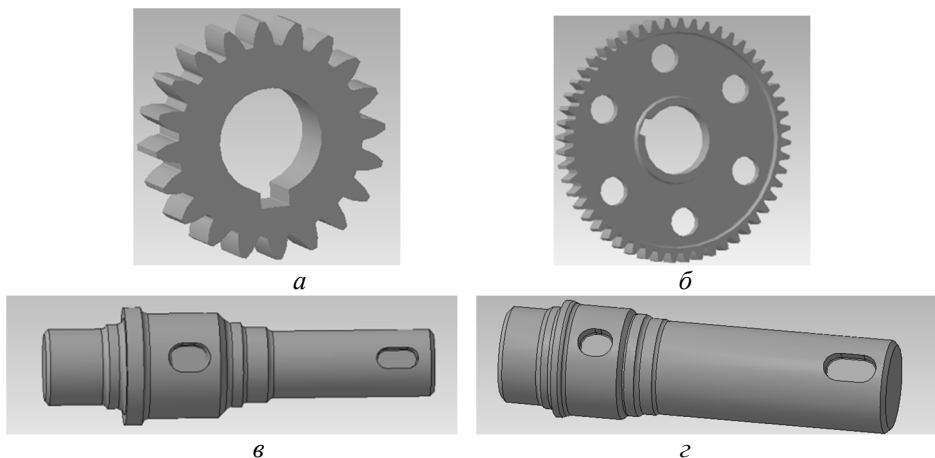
3D моделі деталей редуктора: *a* – шестерня; *б* – зубчате колесо; *в* – бистрохідний вал; *г* – тихохідний вал
